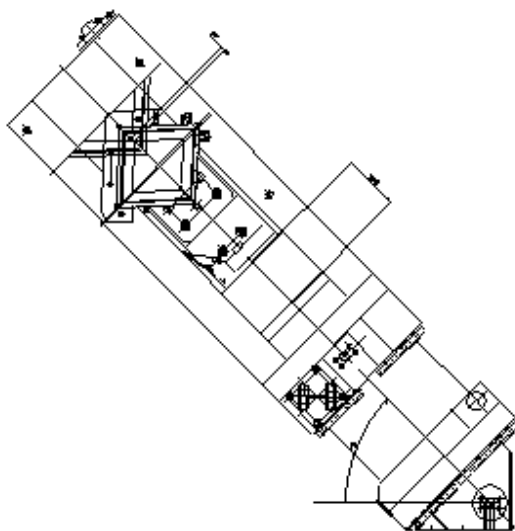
Общий вид гидравлических ножниц поперечной резки на мерные длины непрерывно-литых заготовок
